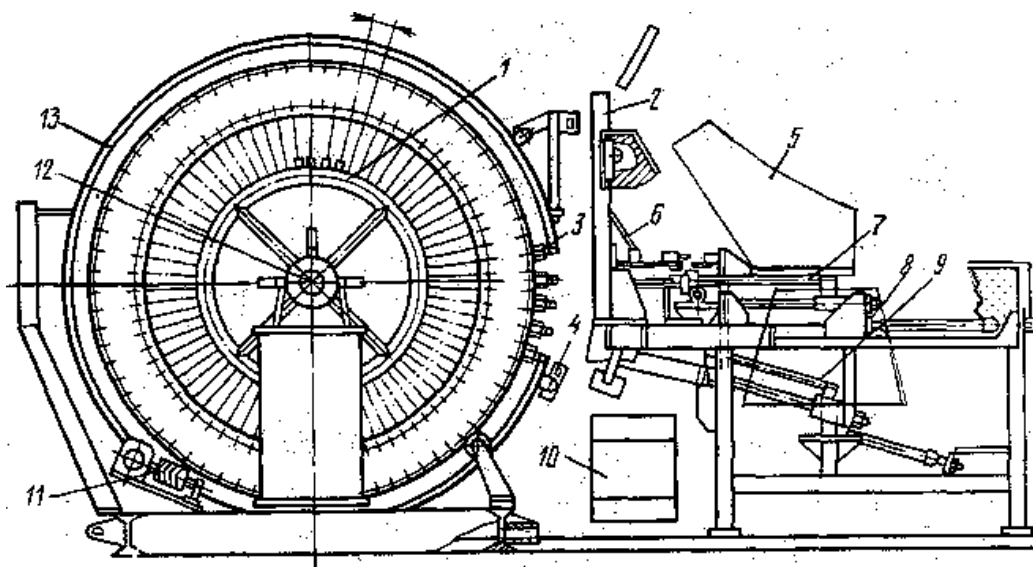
Роторный морозильный аппарат: 1 – кольцевой коллектор для подачи и отвода хладагента; 2 – щит подпрессовывающего устройства; 3 – морозильная плита; 4 – лоток; 5 – весы; 6 – подпрессовывающее устройство; 7 – механизм передвижения стола; 8 – загрузочное устройство; 9 – механизм выгрузки замороженных блоков; 10 – конвейер; 11 – привод; 12 – вал ротора; 13 – бандаж ротора
